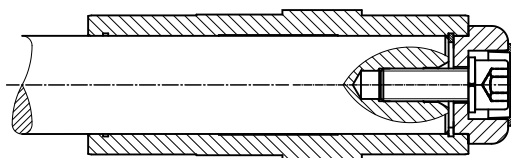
riduttore fissato ad un albero senza spallamento mediante elemento di fissaggio
